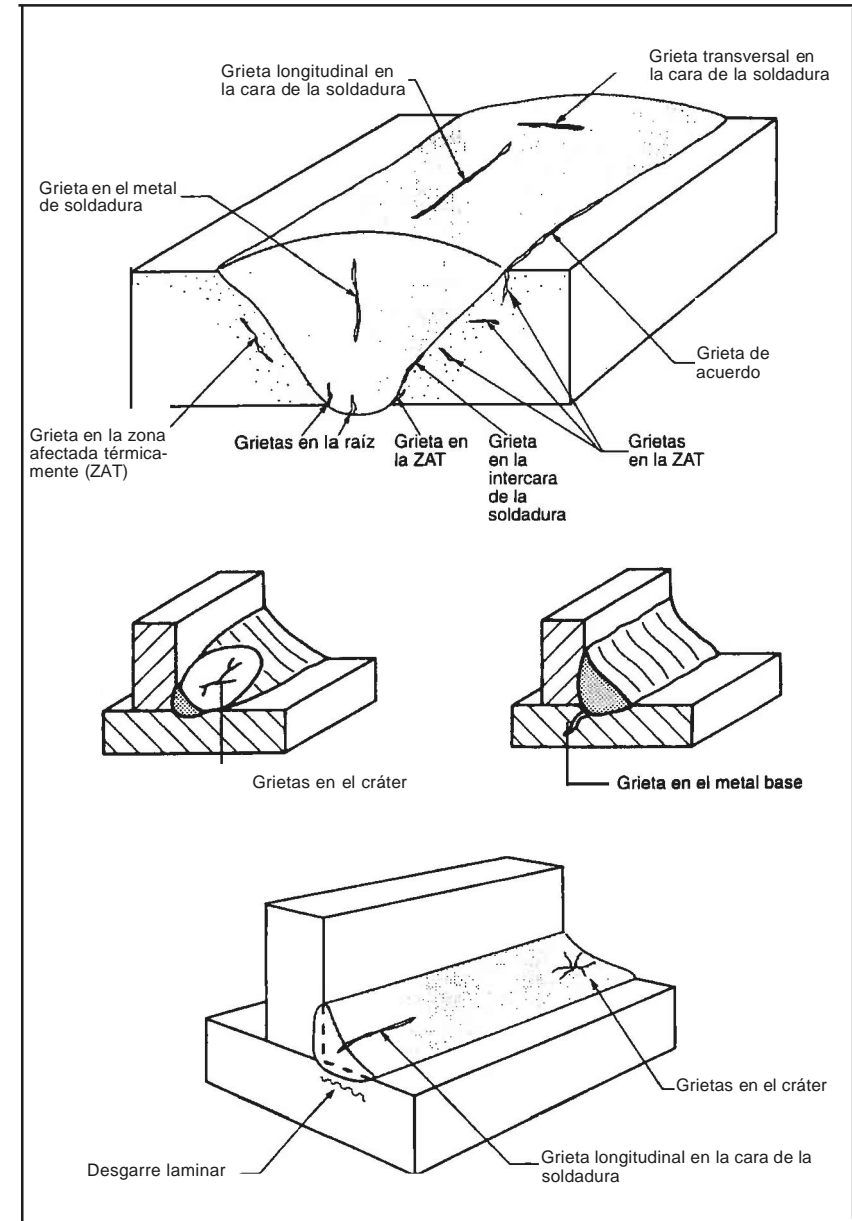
GRIETAS EN LAS SOLDADURAS
